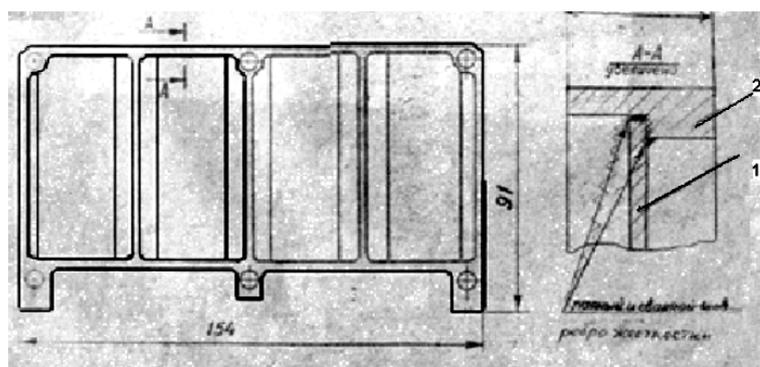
Конструкция рамки: 1 - планка; 2 - рамка
